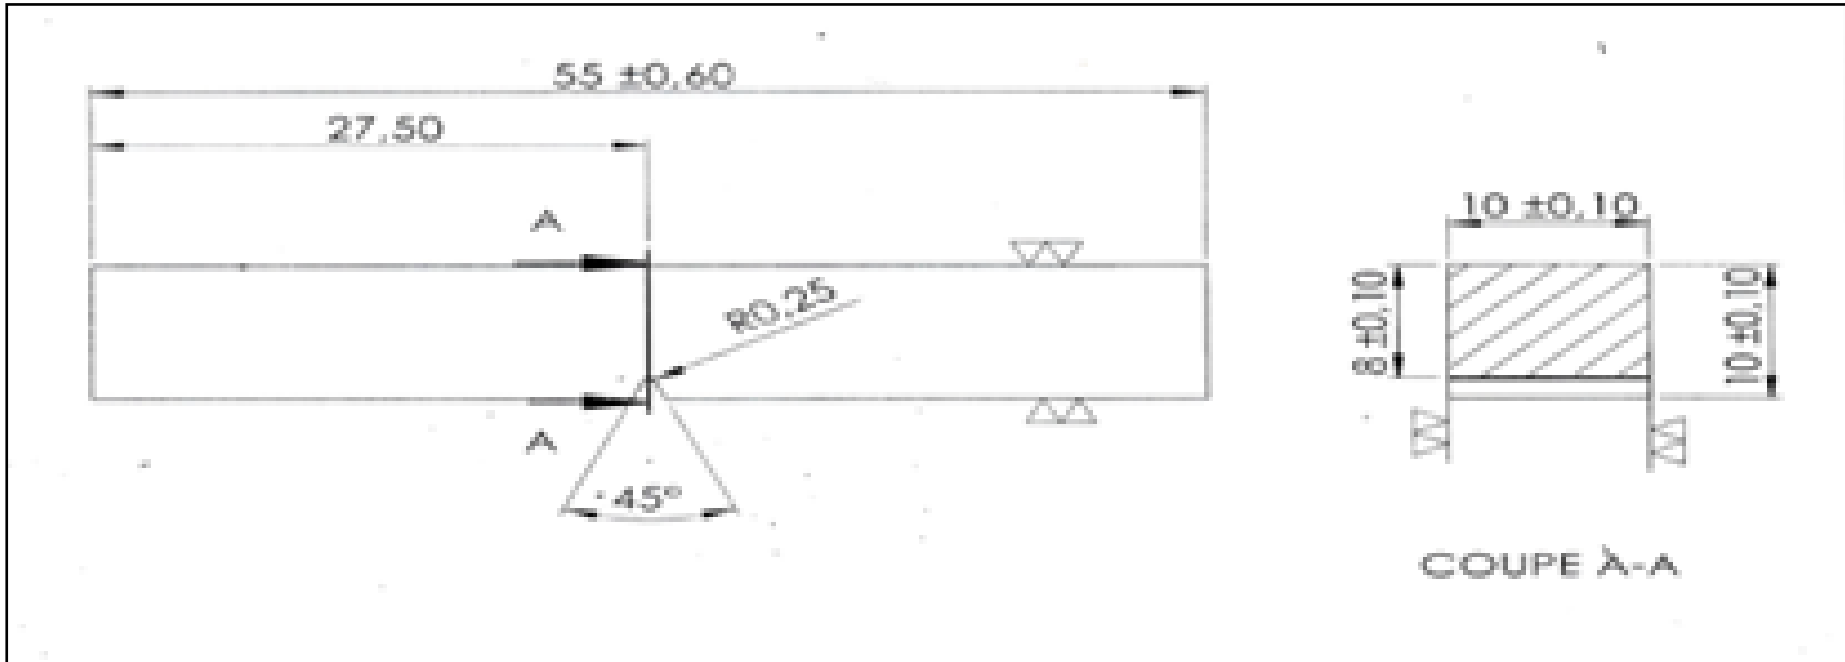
Dimensions technique des éprouvettes destinées à l'essai de resilience
